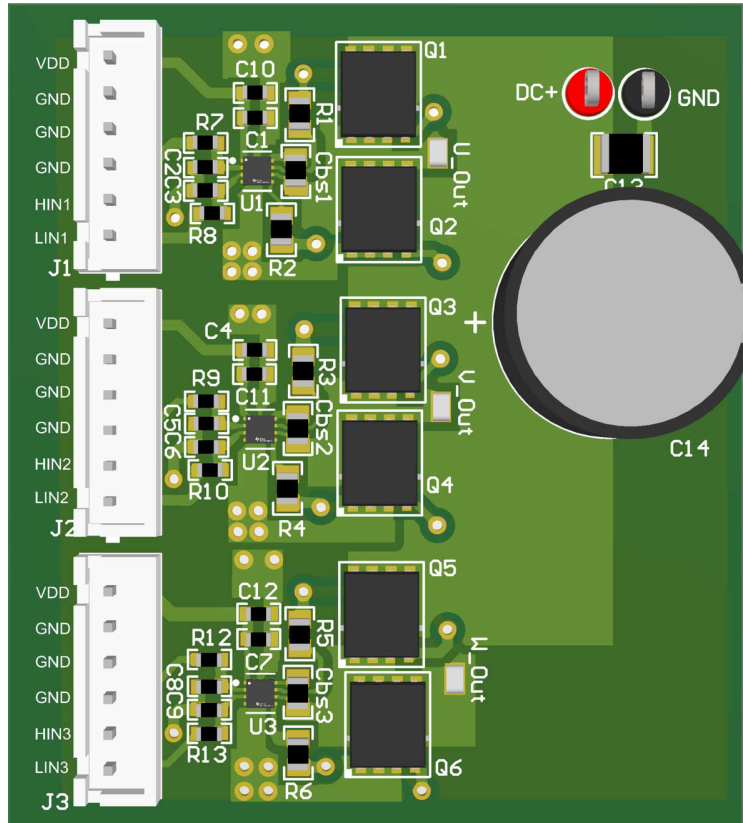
使用三个 LM2105DSGR 半桥驱动器的 BLDC 电机驱动器 PCB 布局示例
